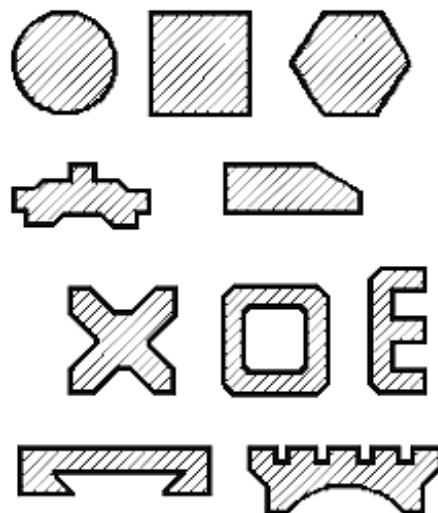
Образцы отливок, полученных непрерывным литьем
